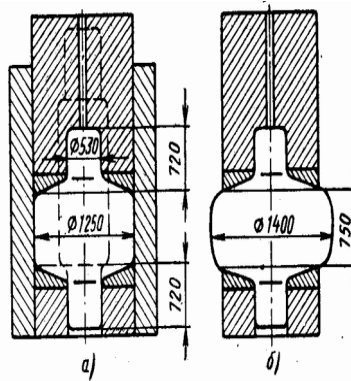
Інструмент для оформлення бочки ротору у процесі ковки
